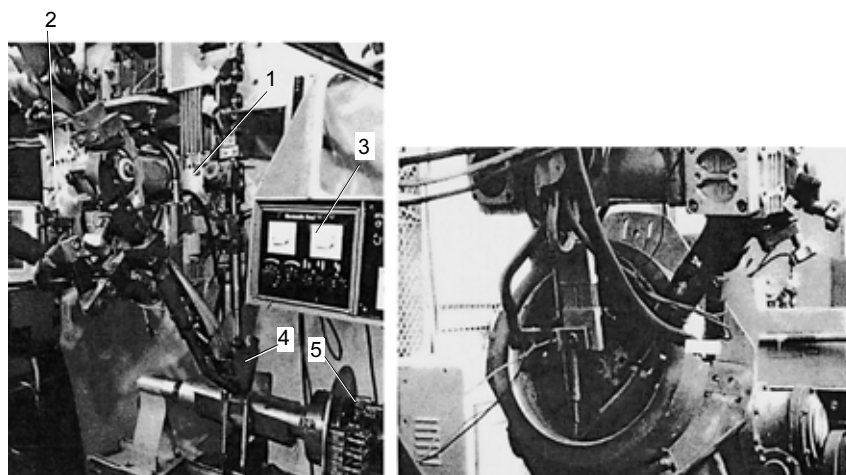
Установка для двухэлектродной наплавки под флюсом с подачей дополнительной заземленной проволоки (а) и наплавка внутренней поверхности трубы (б): 1 — подающий механизм основной проволоки; 2 — подающий механизм дополнительной заземленной проволоки; 3 — пульт управления; 4 — флюсовая воронка; 5 — привод вращения детали
